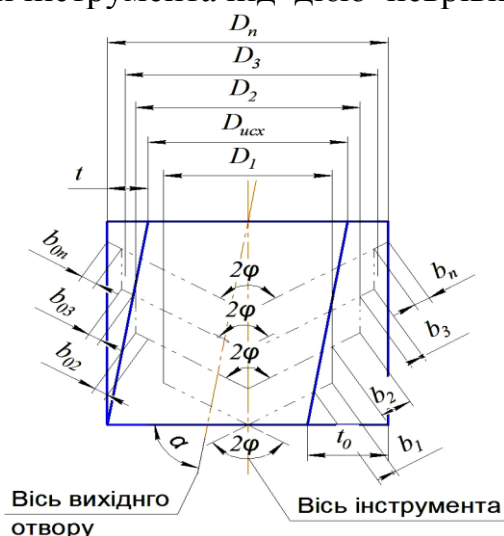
Розрахункова схема для визначення ширини зрізу при обробці ступінчастим КОІ
